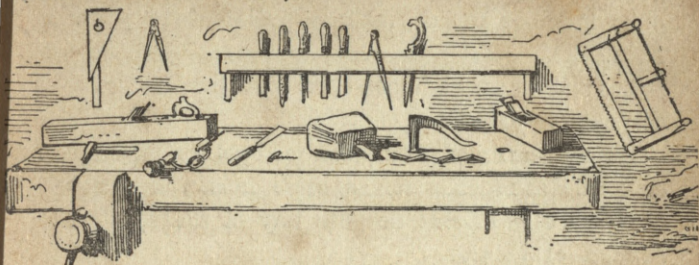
Banco ó taller de un carpintero y sus herramientas.
